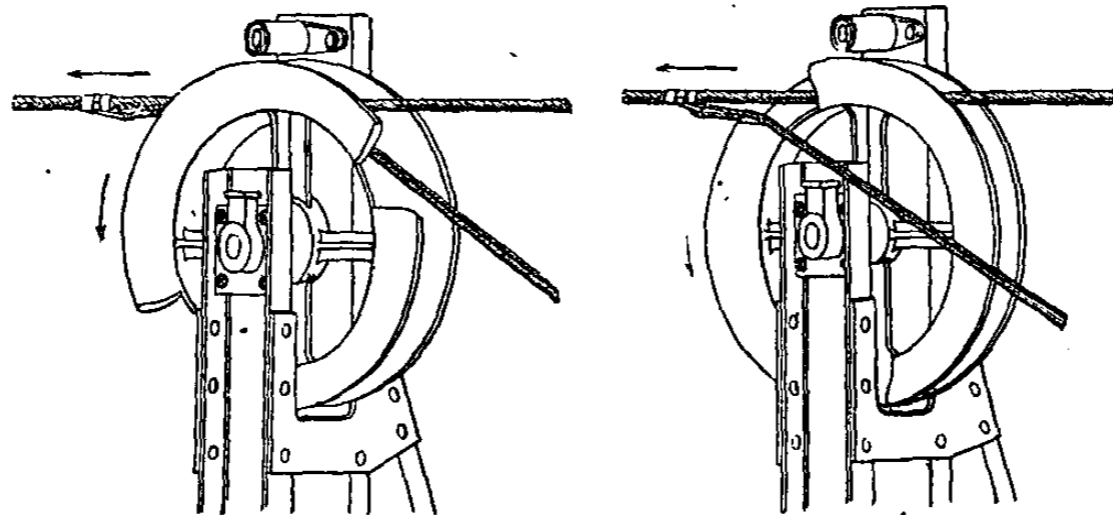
et 566. — Poulies de support du câble. Engagement et déengagement de l'amarre.
